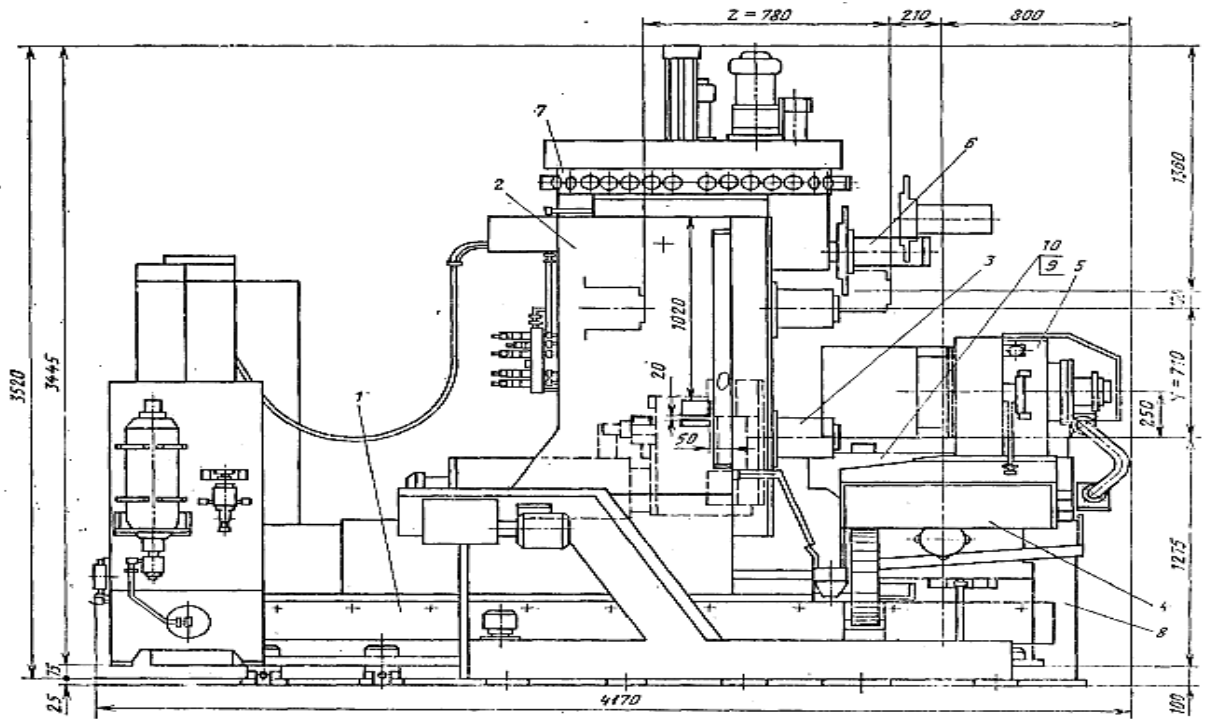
Загальний вид IP500 ПМФ4
